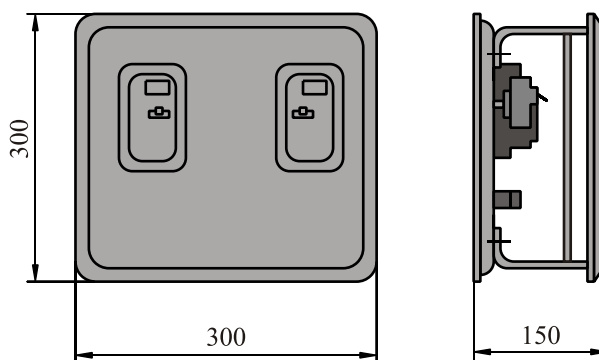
Внешний вид и габаритные размеры щитка ЩЭ1409-01
